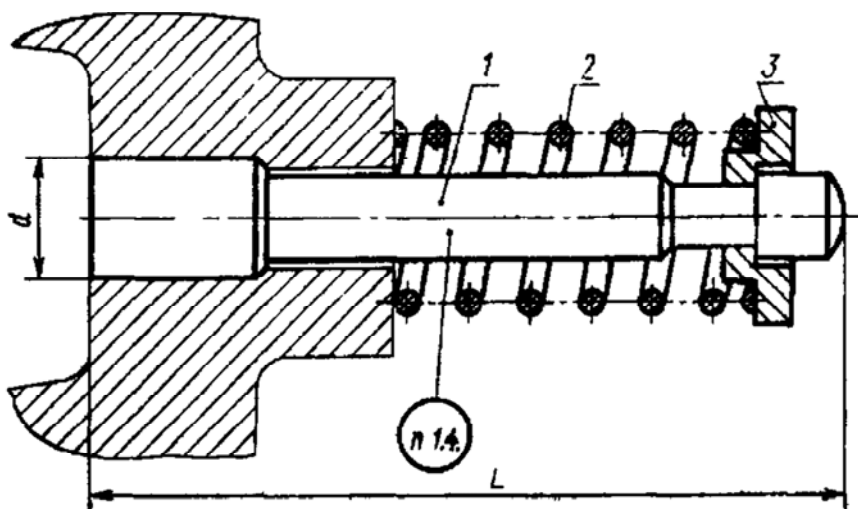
Конструкция пружинного механизма выталкивания:
